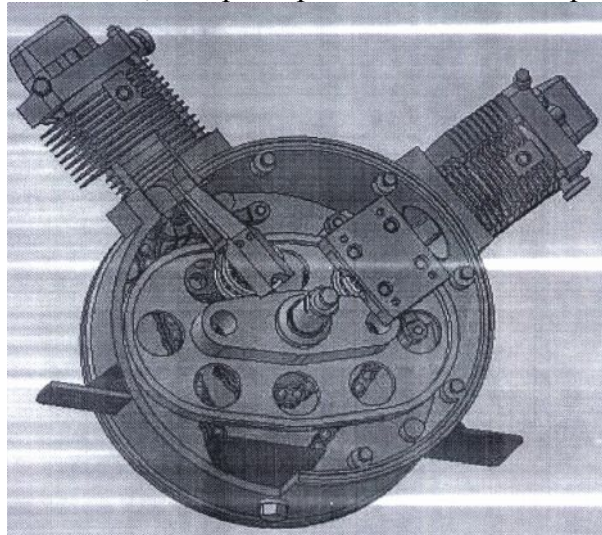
Двухцилиндровый двигатель с радиально-кулачковым механизмом преобразования движения
